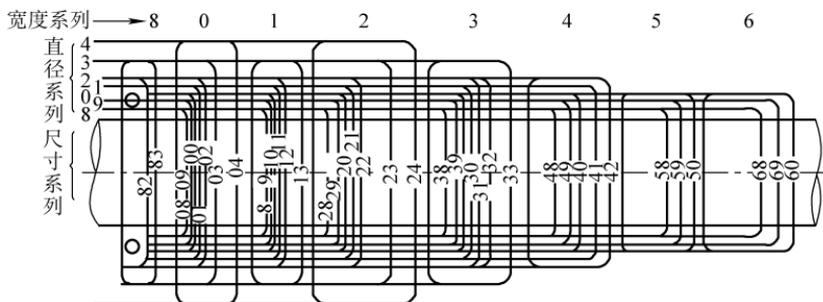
向心滚动轴承常用尺寸系列示意图（圆锥滚子轴承除外）
